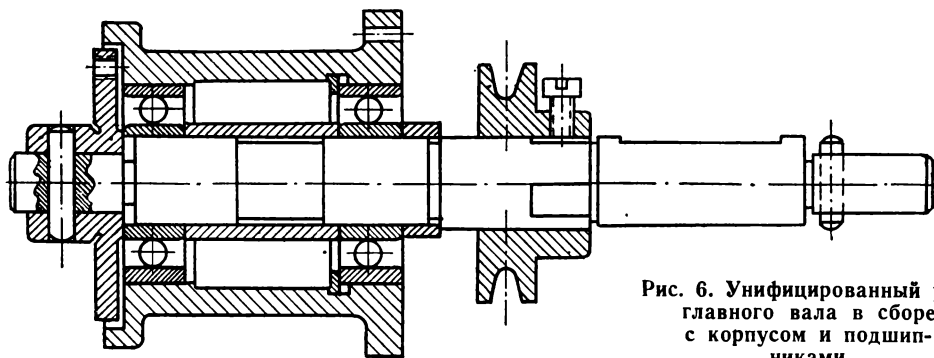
Унифицированный узел главного вала в сборе с корпусом и подшипниками
